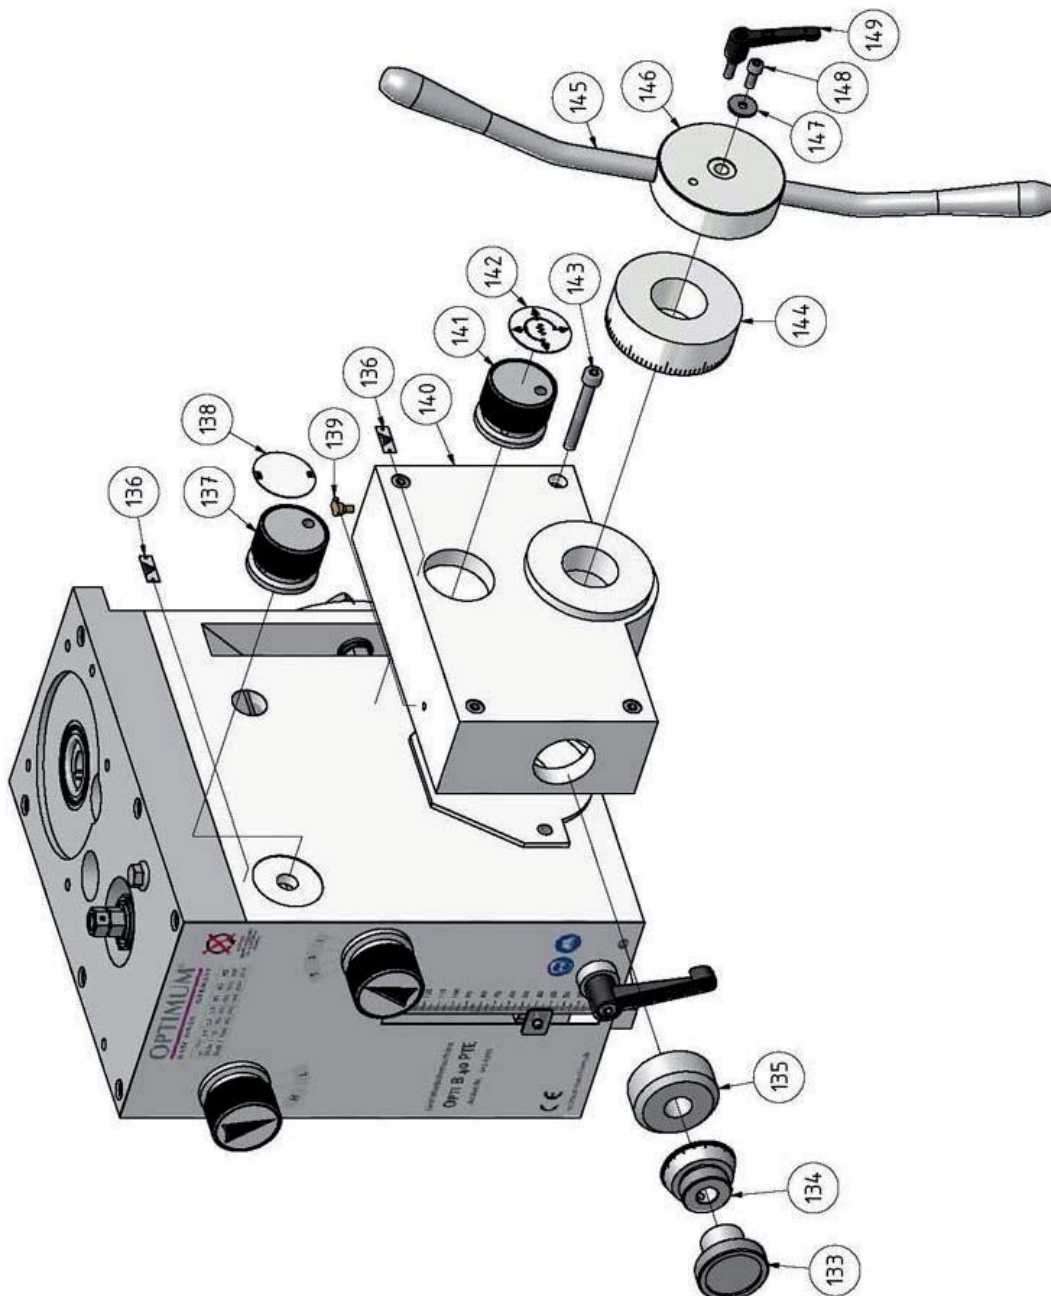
Bohrkopf 7 von 7 - Drilling head 7 von 7- B40PTE
